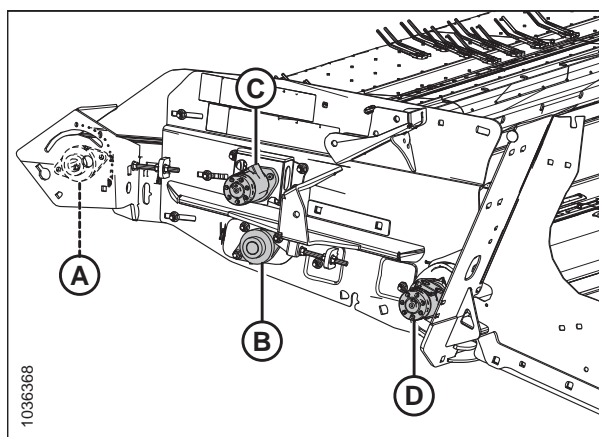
Подшипники роликов полотна — левая сторона
